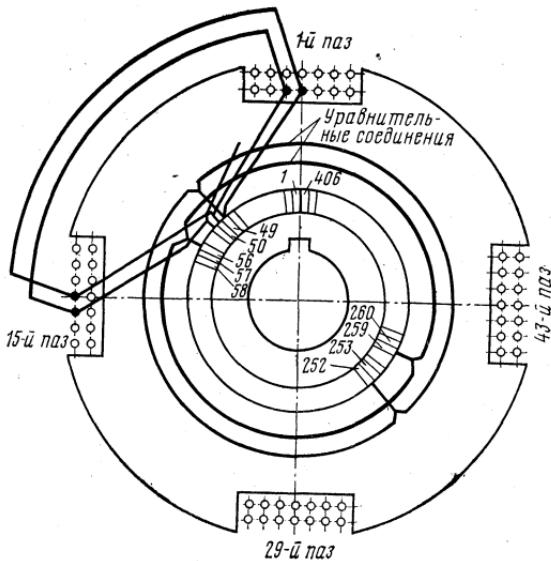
Схема соединения обмотки якоря с коллекторными пластинами тягового двигателя НБ-406Б
